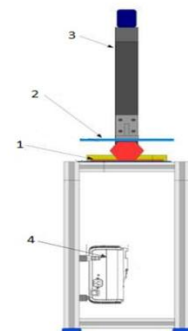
Кінематична схема принтера зі зворотнім DLP 3D-друком
